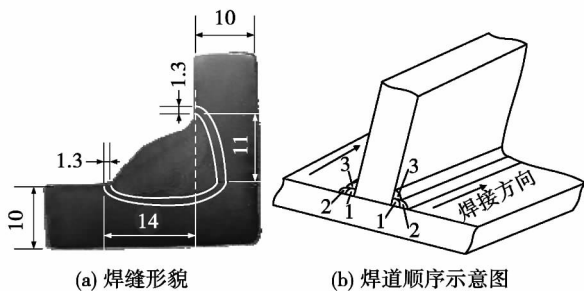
焊缝形貌和焊道顺序示意图 (mm)
